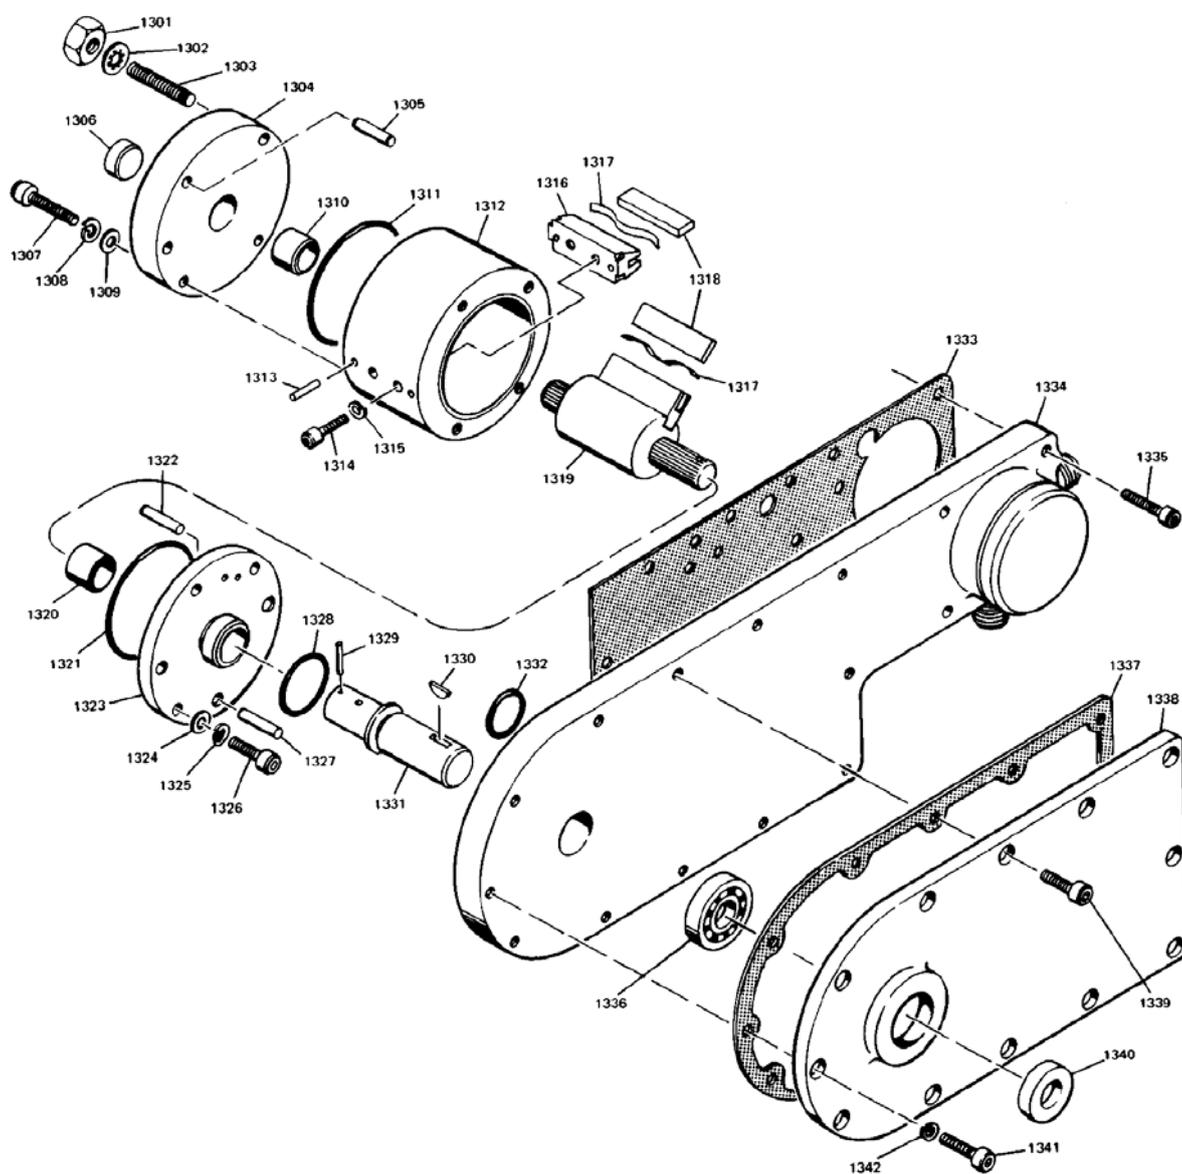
Explosionsdarstellung des Drehflügelmotors
